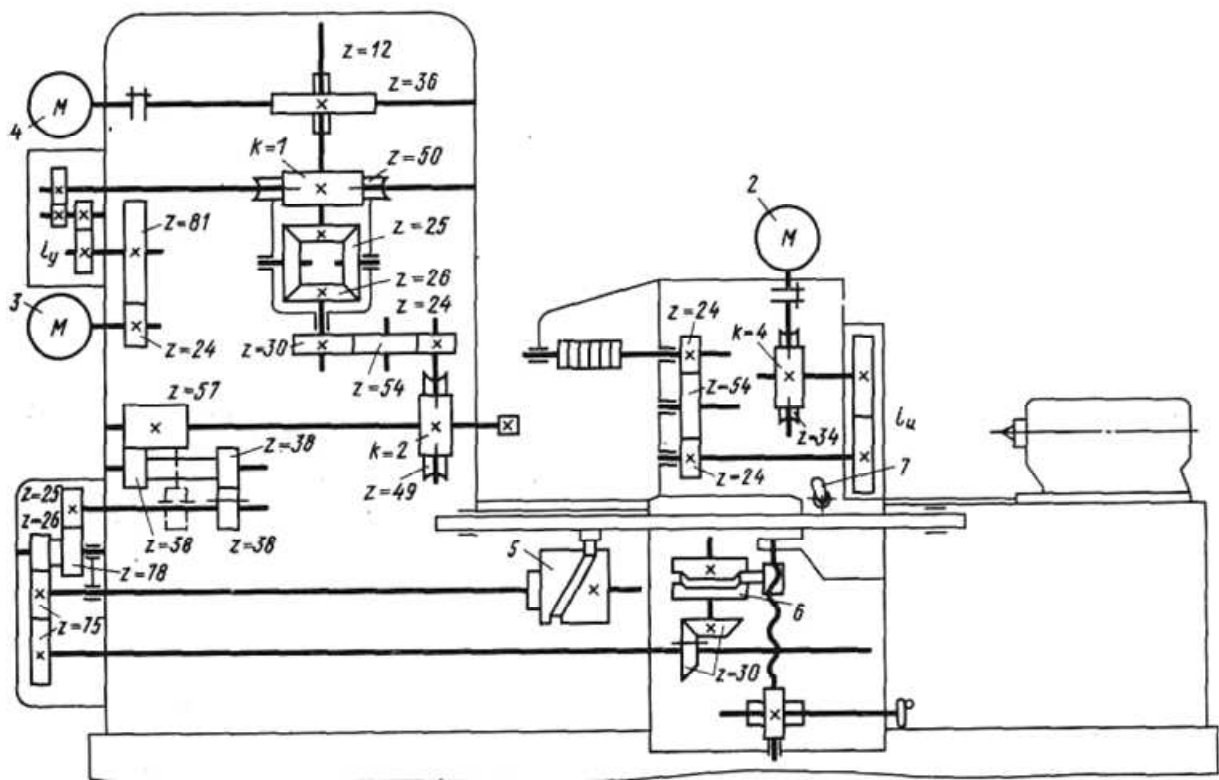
Кинематическая схема резьбофрезерного станка для обработки коротких резьб
